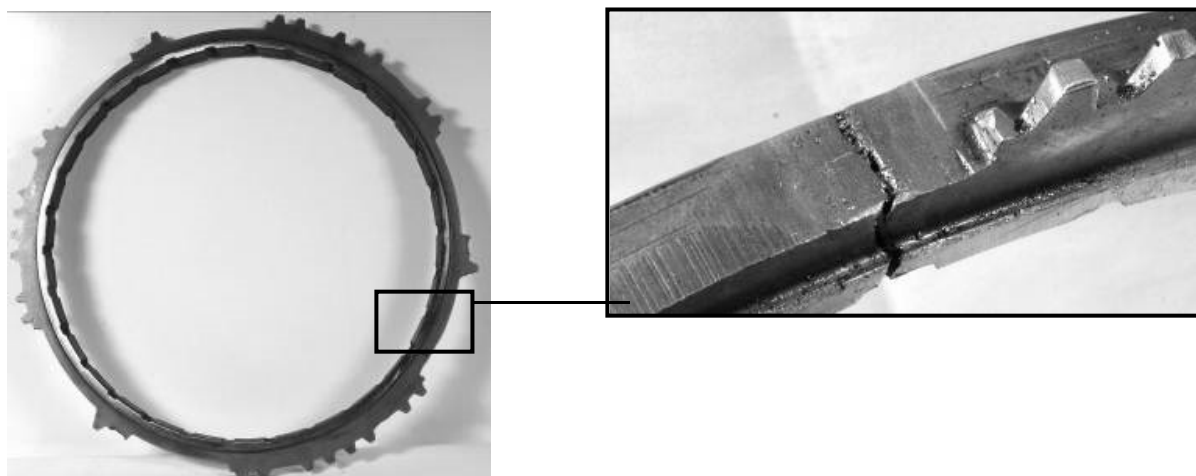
Усталостное разрушение блокировочного кольца синхронизатора КПП
